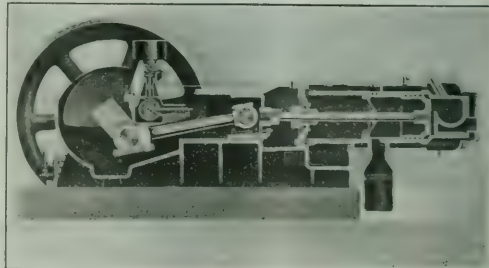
MOTOR SEMI-DIESEL HORIZONTAL BUCKEYE
